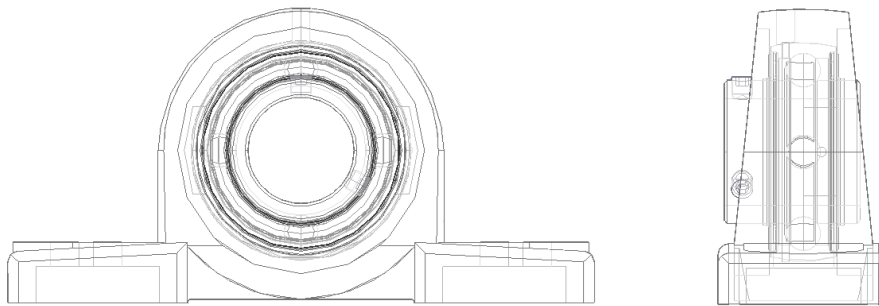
Vista lateral y frontal de Rodamiento del eje B.
